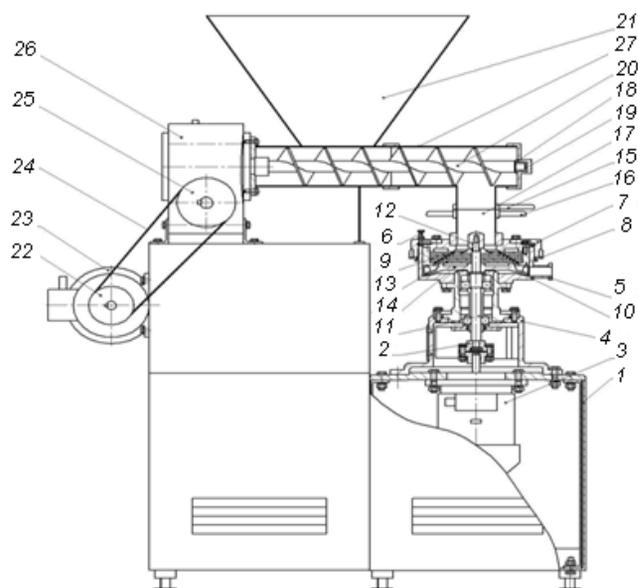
Агрегат для тонкого измельчения творога: 1 — рама; 2 — муфта; 3 — электродвигатель; 4 — юбка; 5 — выгрузочная горловина; 6 — стопорный винт; 7 — резьбовое кольцо; 8 — обойма неподвижных ножей; 9 — неподвижные ножи; 10 — корпус ножевой головки; 11 — вал; 12 — прижимная гайка; 13 — подвижные ножи; 14 — разгрузочный диск; 15 — фиксирующая гайка; 16 — контргайка; 17 — загрузочная горловина; 18 — крышка; 19 — подшипник скольжения; 20 — шнек; 21 — загрузочный бункер; 22 — ведущий шкив; 23 — электродвигатель; 24 — ремень клиновой; 25 — ведомый шкив; 26 — червячный редуктор, 27 — корпус
